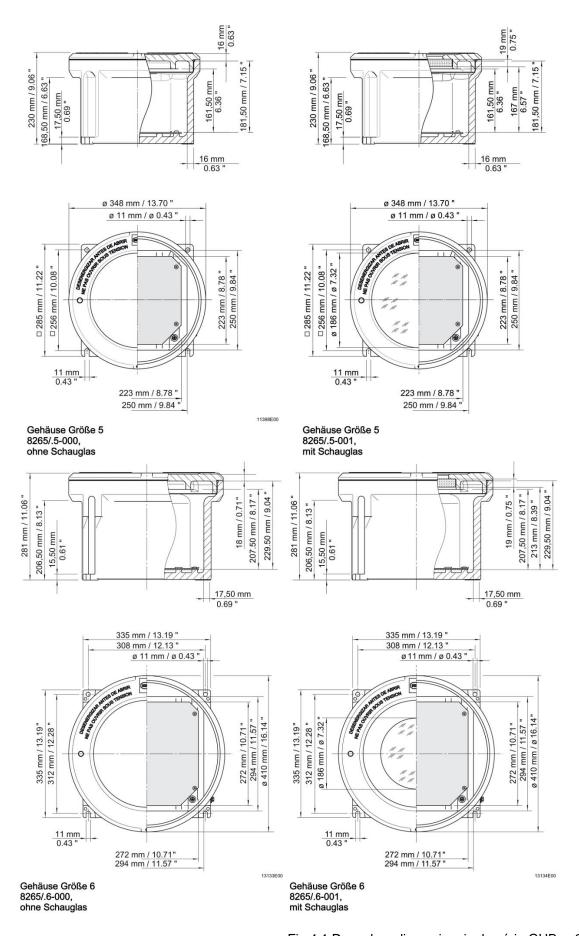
Desenhos dimensionais da série GUBox 8265
